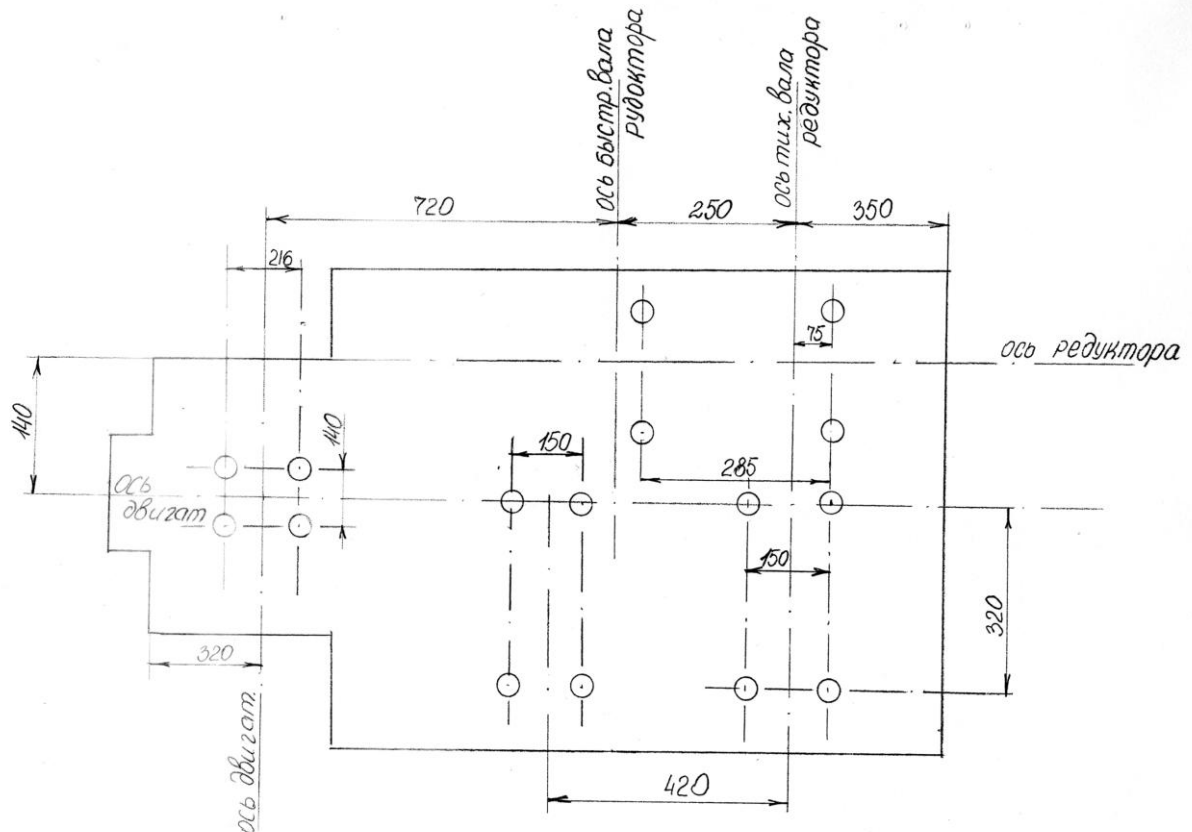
Схема геодезичного обґрунтування монтажу
